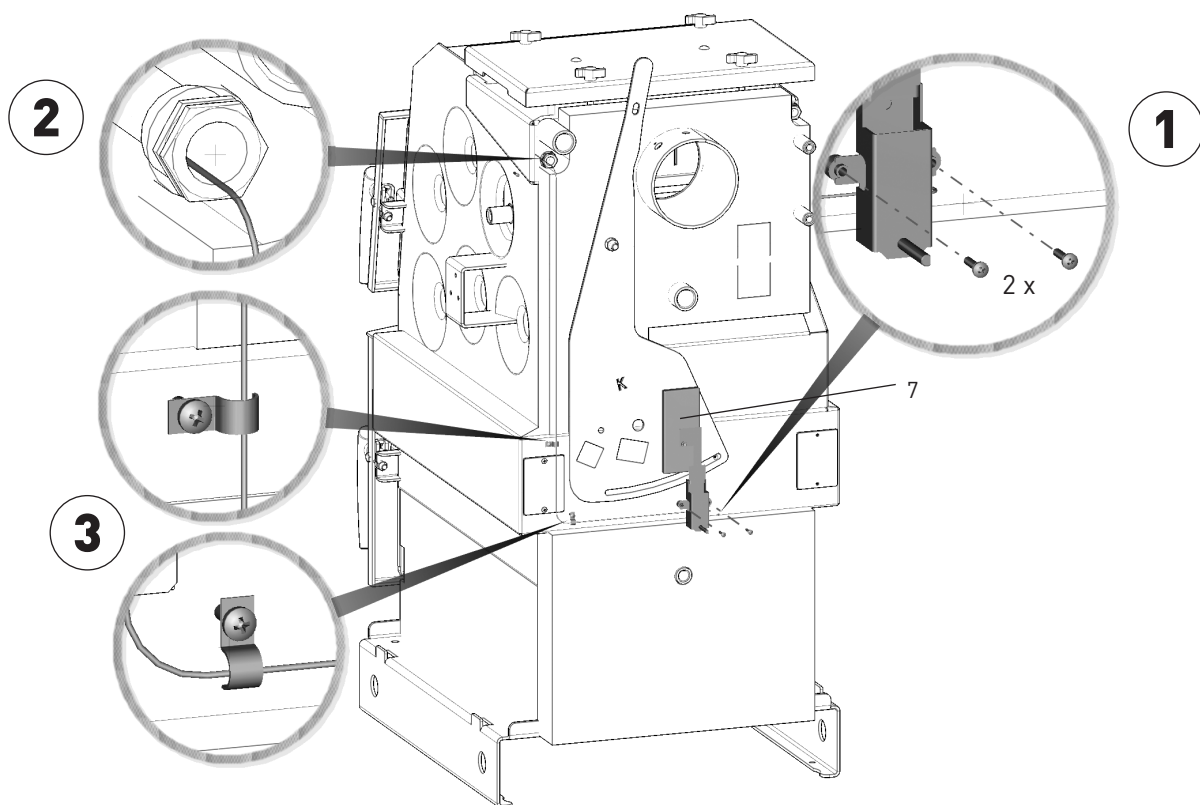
Installazione caldaia e passaggio cavo controllo combustione nell'alloggiamento - vista posteriore.
